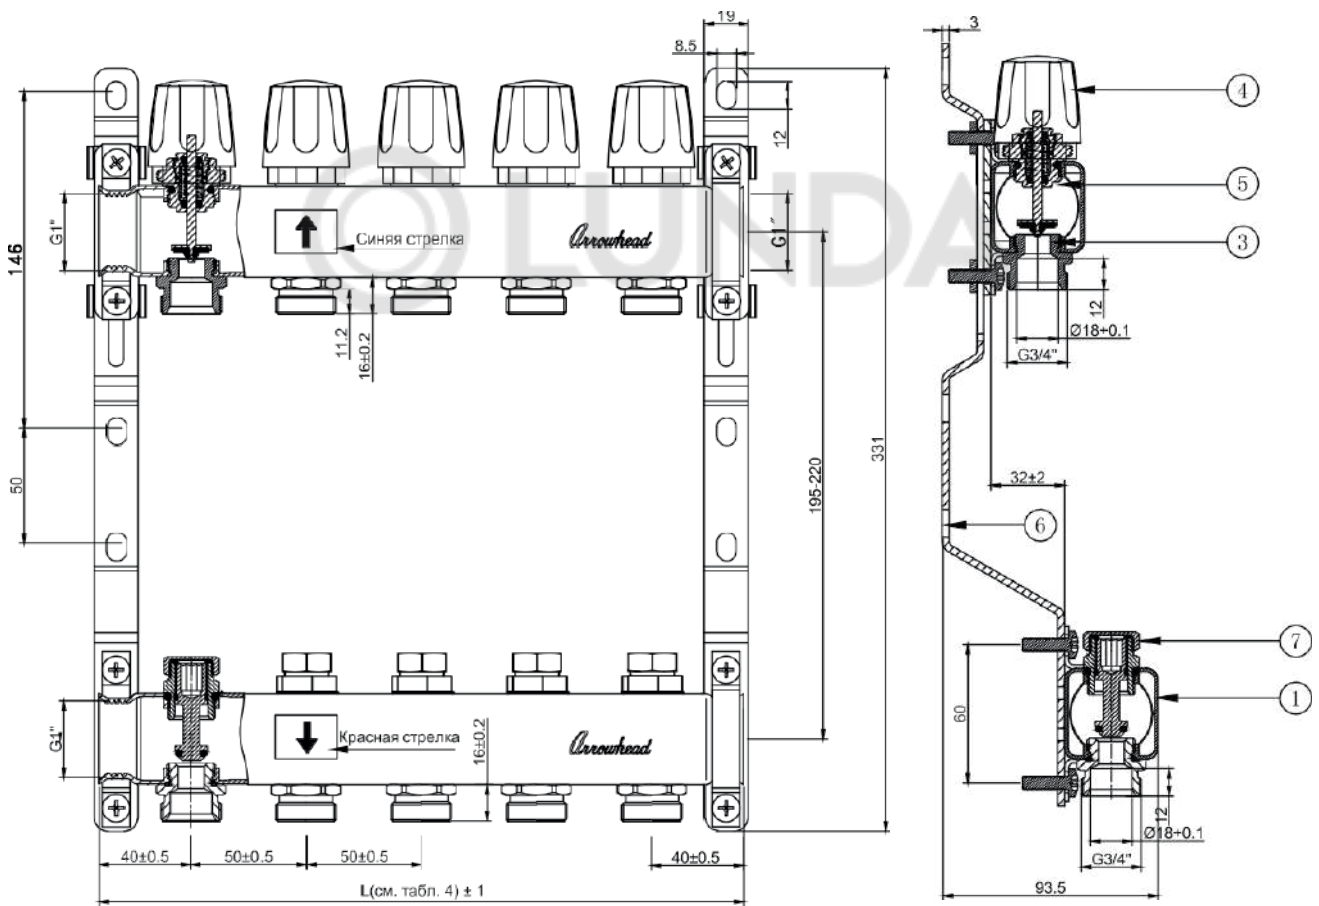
Основные детали и габариты коллекторов серии CS-300-xx ARROWHEAD
